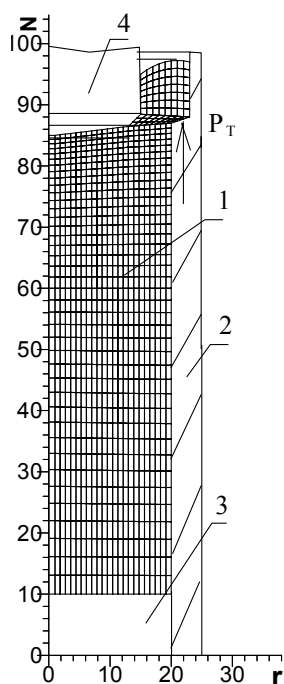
Вихідний стан заготовки перед видавлюванням (розміри в міліметрах)
